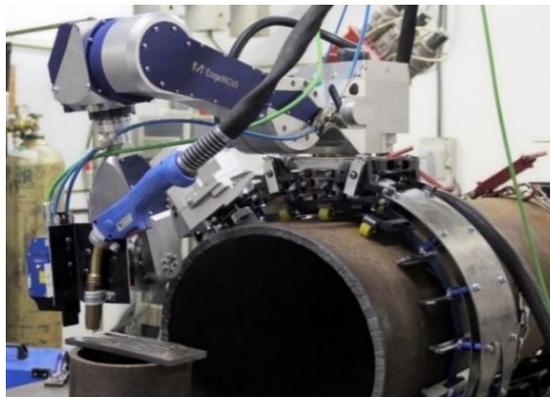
Sistema de soldagem concebido em conjunto com LABSOLDA, SENAI, Petrobras e EngeMovi
